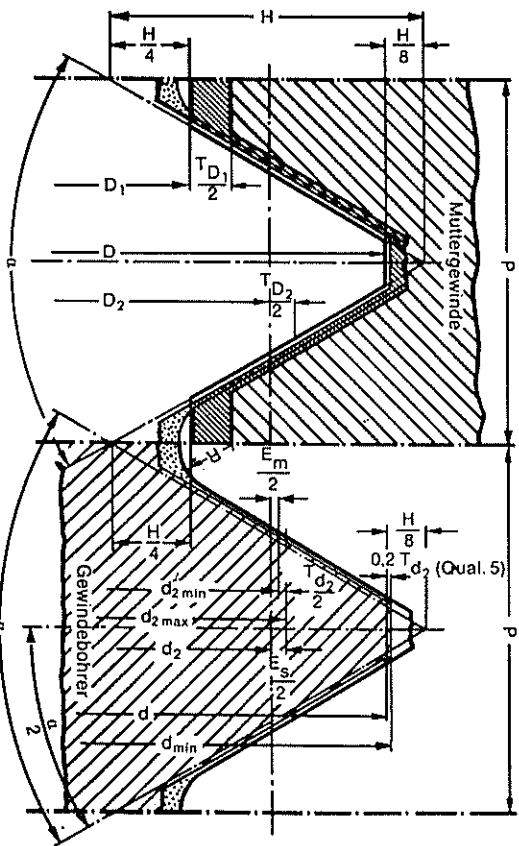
Maße und Toleranzen am Muttergewinde und am Gewindebohrer
